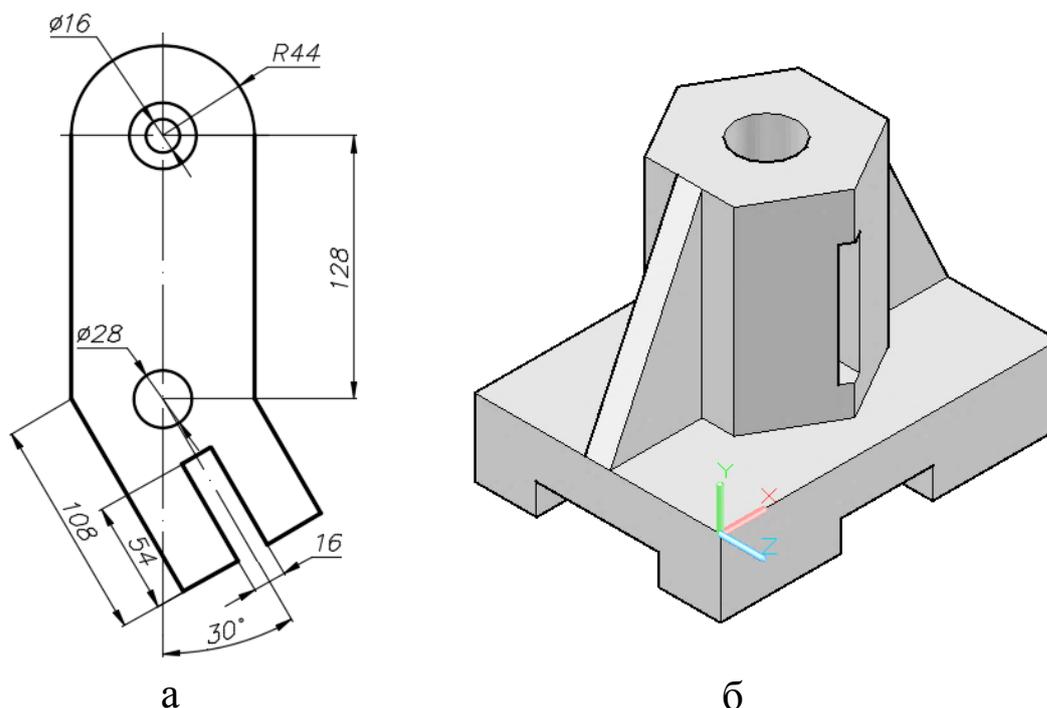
Фрагмент двухмерного чертежа (а) и трехмерная модель детали (б), выполненные с использованием Autodesk AutoCAD
